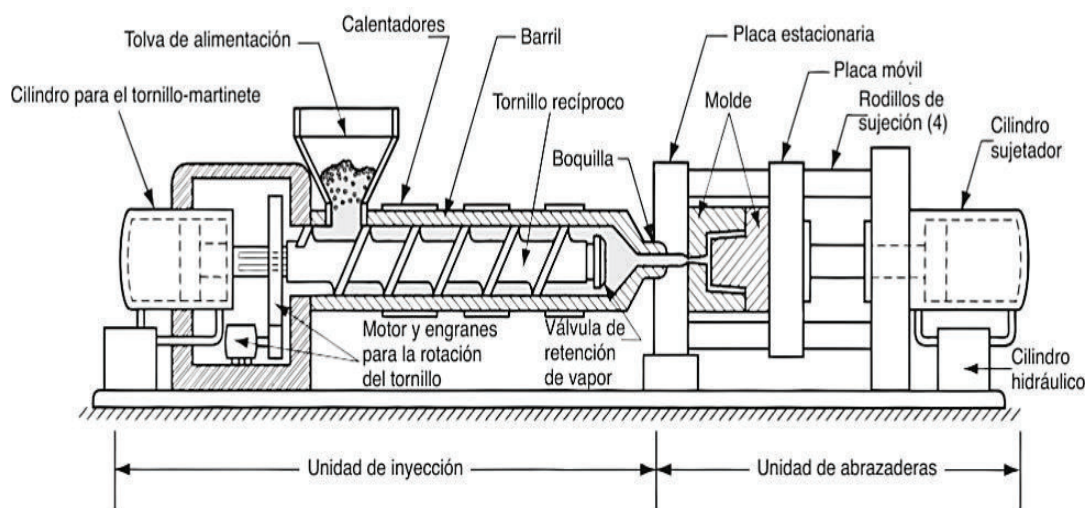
Diagrama de una máquina de moldeo por inyección
